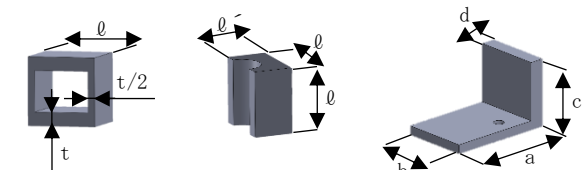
(a)に示す正方形のセルを1列に5ユニット繋げ、先端に図1(b)のおもり取り付け部を加えた長さ  $5\ell + \ell'$  の梁部分に、図1(c)の部品を接続した片持ち梁のモデルを3D-CADにより作成する。それをAMで造形し、実験対象とする。今回使用するAMは、熱溶解積層方式(FDM: Fused Deposition Modeling)のDreamer(FLASHFORGE社製)である。片持ち梁の材料にはABS樹脂を用いる。またサポート材料については、除去を容易にするため、リモネンという溶剤で溶かすことが可能なHIPS(耐衝撃性ポリスチレン)を用いる。
